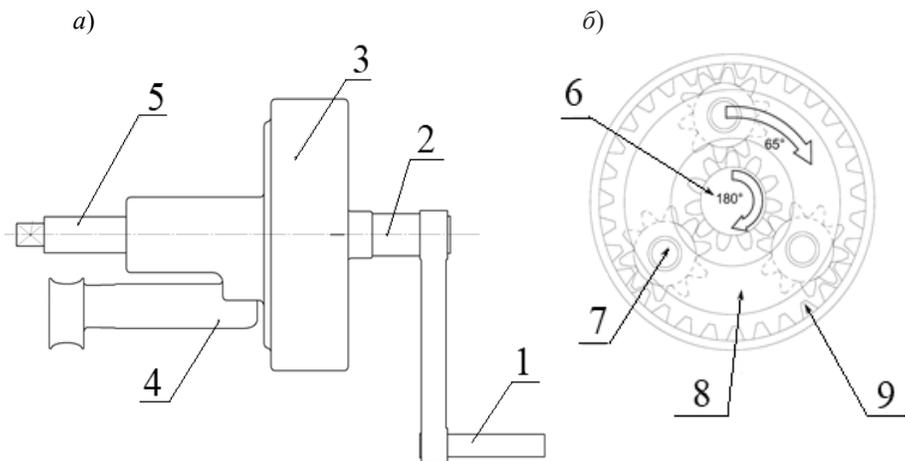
Общий вид (а) и схема планетарного редуктора (б) устройства для отворачивания и заворачивания гаек колес и стремянок рессор
